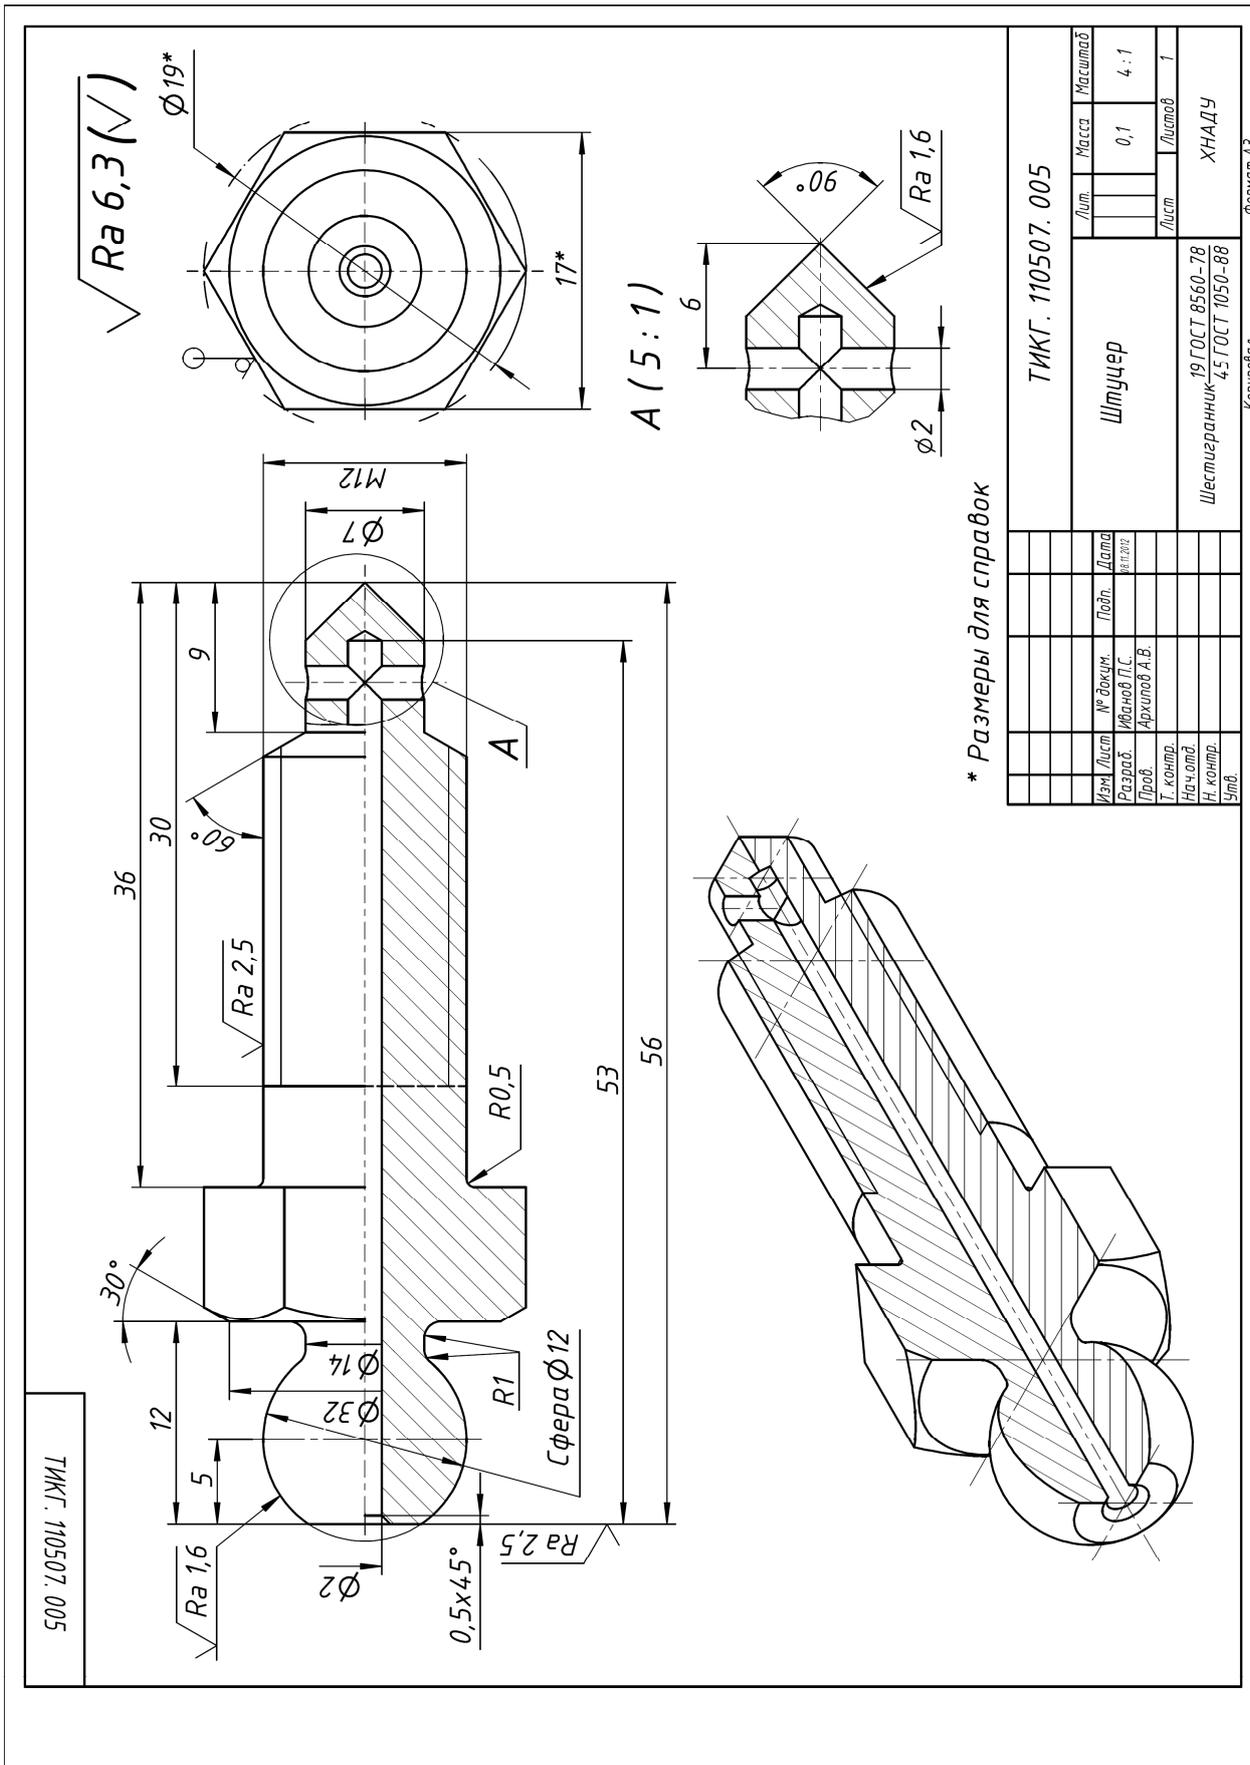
Чертеж детали штуцер с аксонометрией
